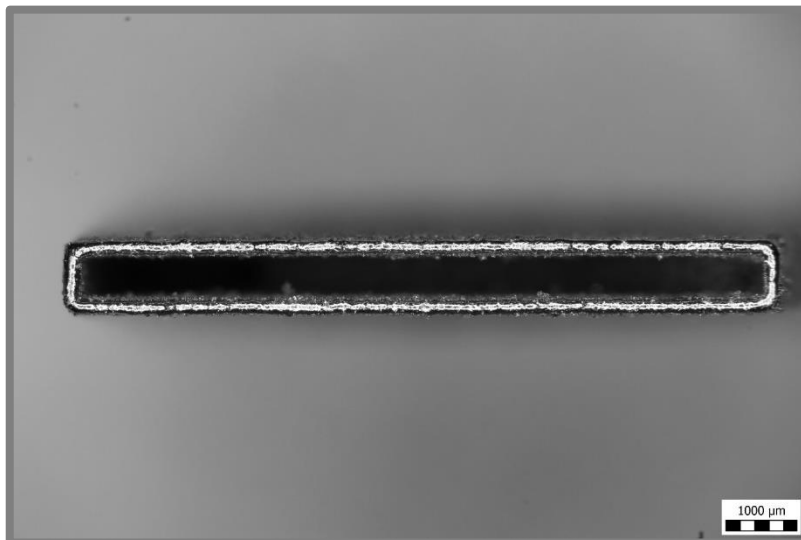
Snímek vzorku v horním pohledu. Procesní parametry: výkon laseru = 400 W, rychlost skenování = 700 mm/s
